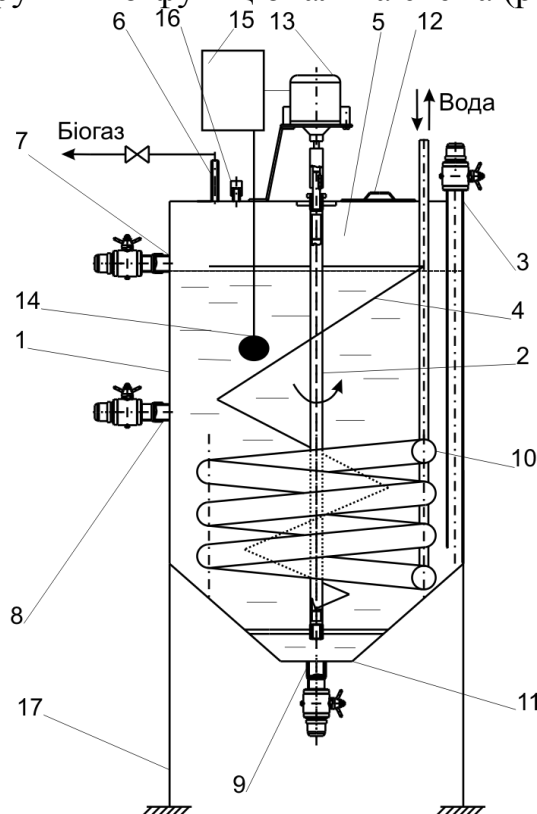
Конструктивно-функціональна схема мікробіологічного реактора: 1 – корпус реактора, ззовні теплоізолюваний; 2 – вал змішувача; 3 – патрубок завантажувальний; 4 – шнек; 5 – газова камера; 6 – патрубок відбору; 7 – зливний патрубок; 8 – резервний патрубок; 9 – патрубок повного зливу; 10 – теплообмінник; 11 – з'ємне дно реактора; 12 – кришка реактора; 13 – електродвигун; 14 – датчик температури; 15 – блок автоматичного керування; 16 – запобіжний клапан; 17 – опора реактора.
